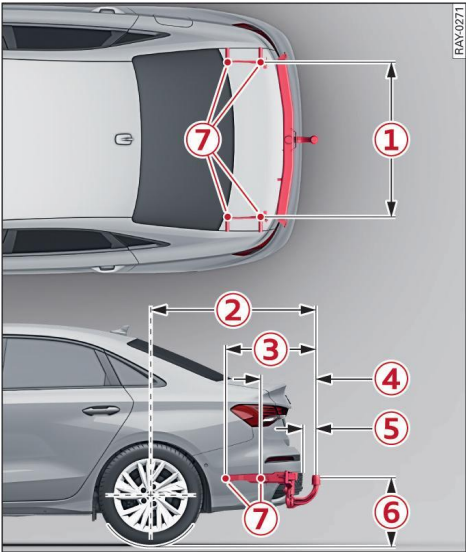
Dispositivo para remolque: Cotas y puntos de montaje
